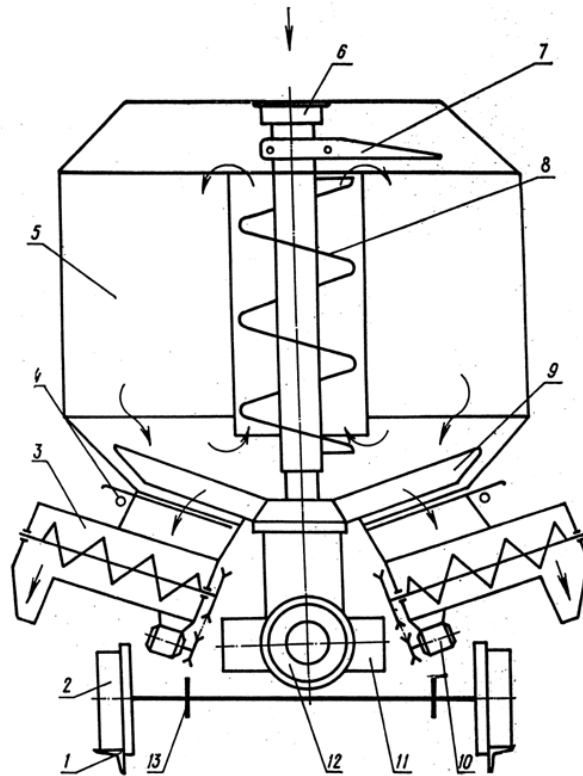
Схема кормороздавача-змішувача КС-1,5: 1 – шлях рейковий; 2 – колеса ходові; 3 – шнек вивантажувальний; 4 – пристрій дозуючий; 5 – бункер; 6 – верхня опора шнекової мішалки; 7 – розрівнювач; 8, 9 – шнекова і лопатева мішалки; 10 – привід вивантажувального шнека; 11 – коробка розподільна; 12 – мотор-редуктор; 13 – ведуча зірочка ходового візка
